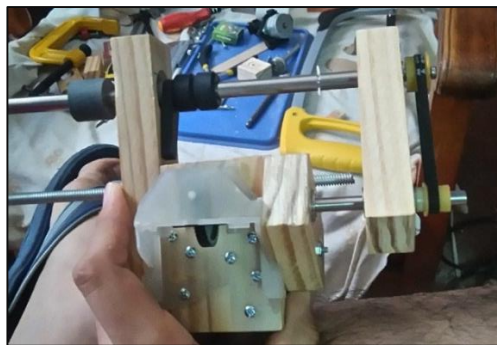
Proceso de ensamblado del motor del eje de ascensión recta.
